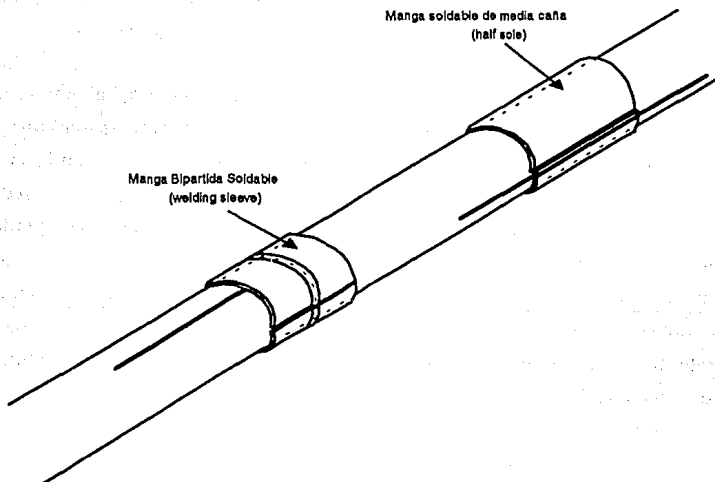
Reparación de poros en soldaduras, transversal de campo y longitudinal de fábrica.
